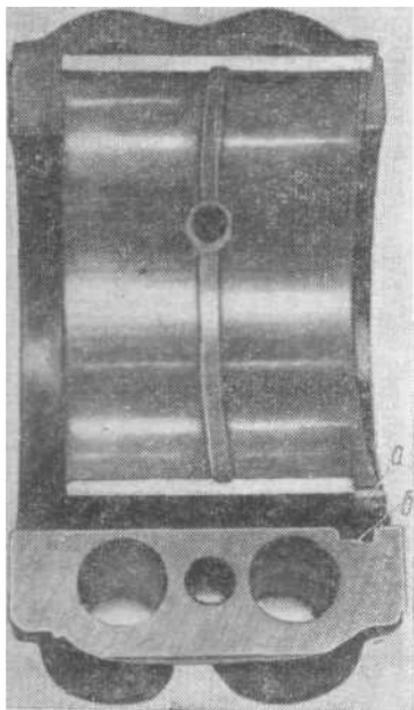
Фиксирующий выступ вкладыша и гнездо для него в крышке подшипника
